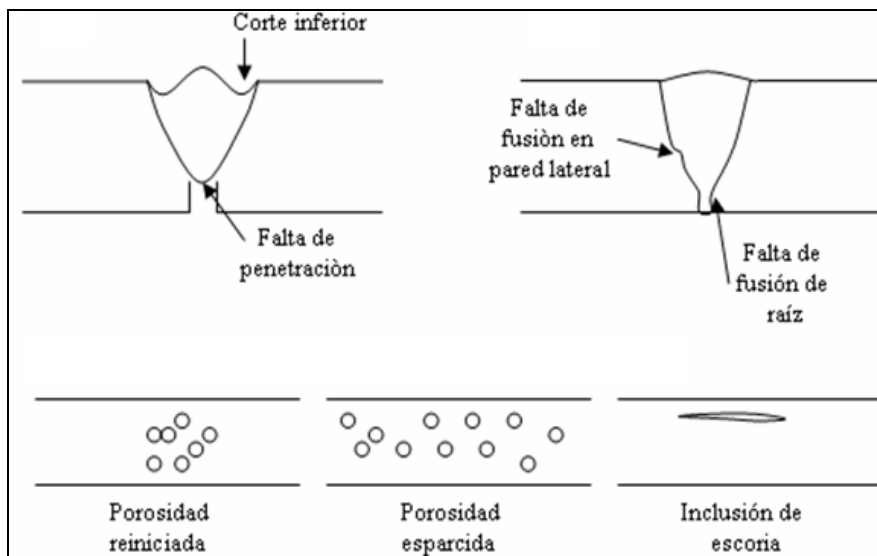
Algunos defectos de la soldadura. [20]
